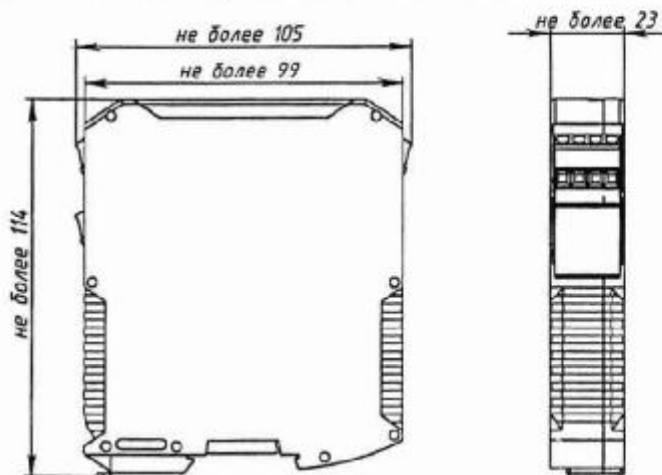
Преобразователь, с конструктивным исполнением Дн для крепления на DIN-рейку с цифровым протоколом, или без цифрового протокола. Степень защиты оболочки IP20.
